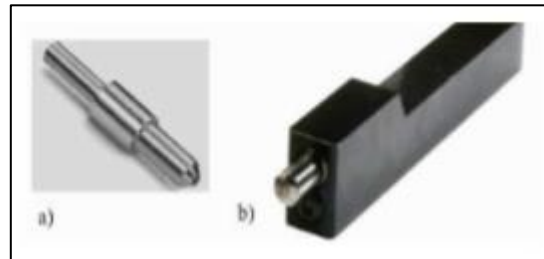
Outil de galetage commercialisé par la firme COGSDILL TOOL : a) partie active, b) corps de l'outil [19]
